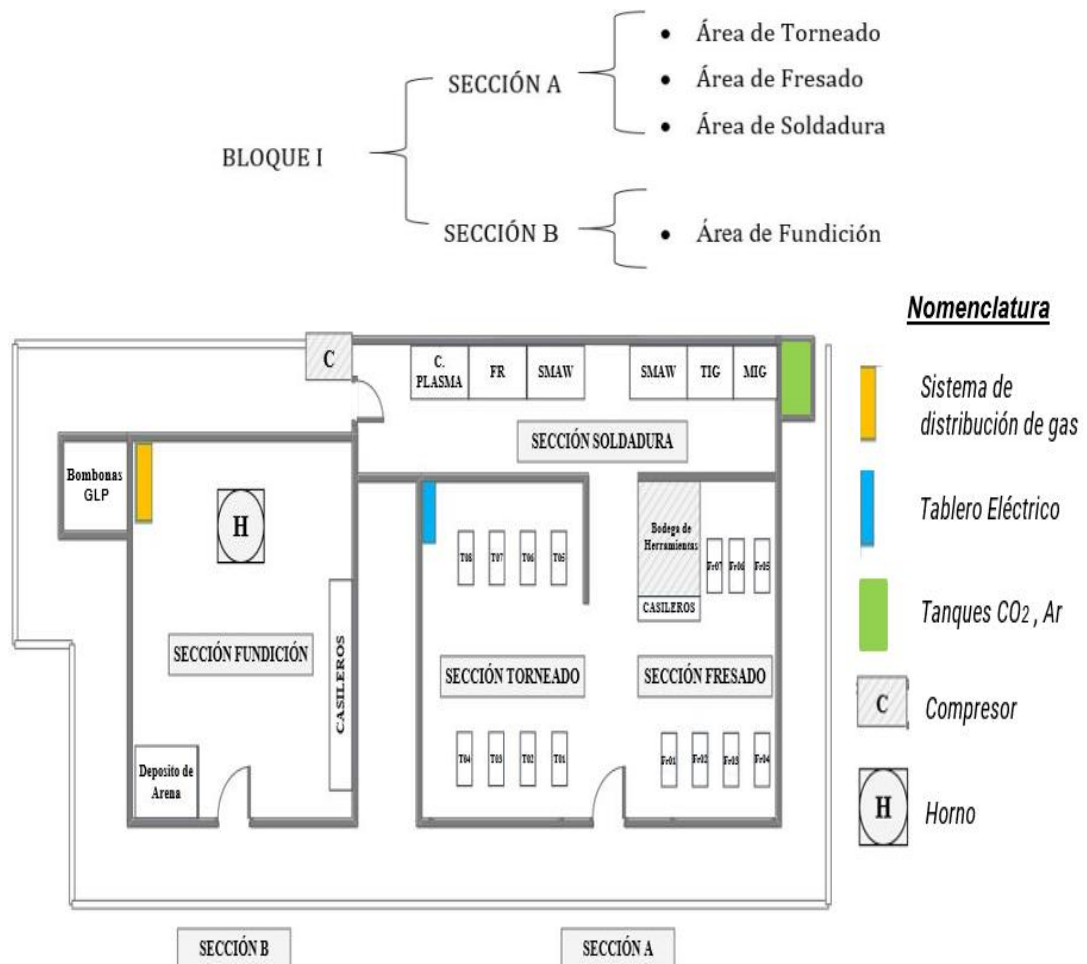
Esquema de planta de la distribución física del Bloque “I”
